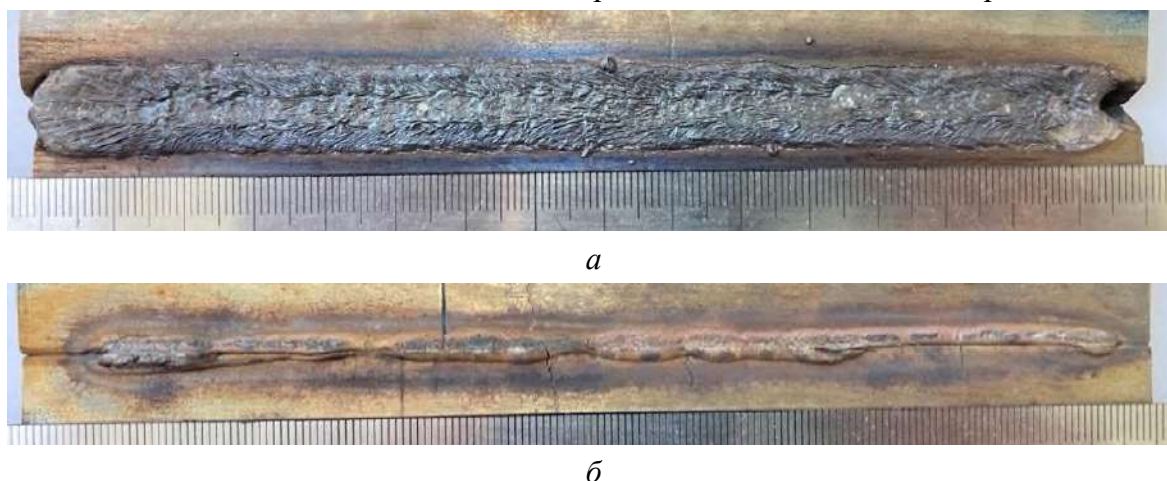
Зовнішній вигляд зварного з'єднання (а) та зворотного формування шва (б) у стані повного охолодження
